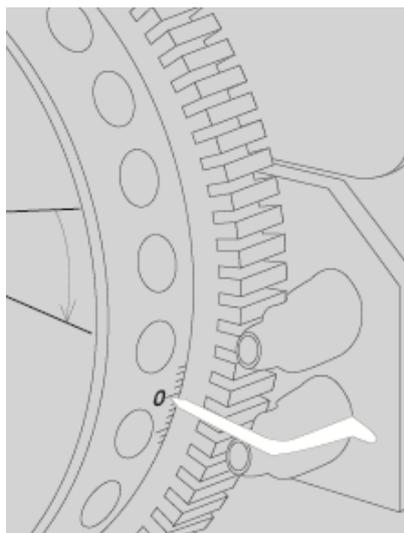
Soporte de los sensores de vueltas y sincronización del motor
